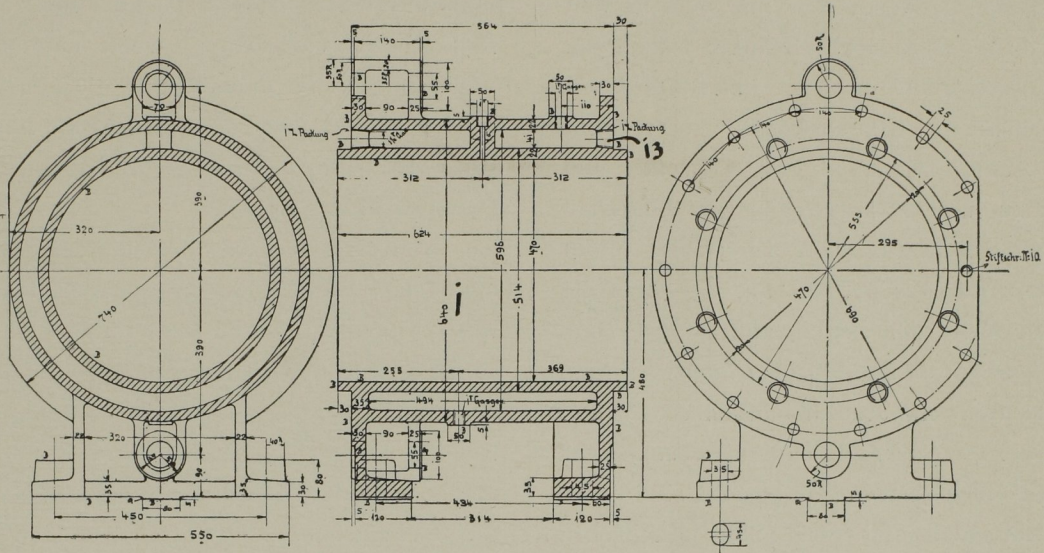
Schnitte und Grundriss des Kompressor-Cylinders. Masst. 1:15.
